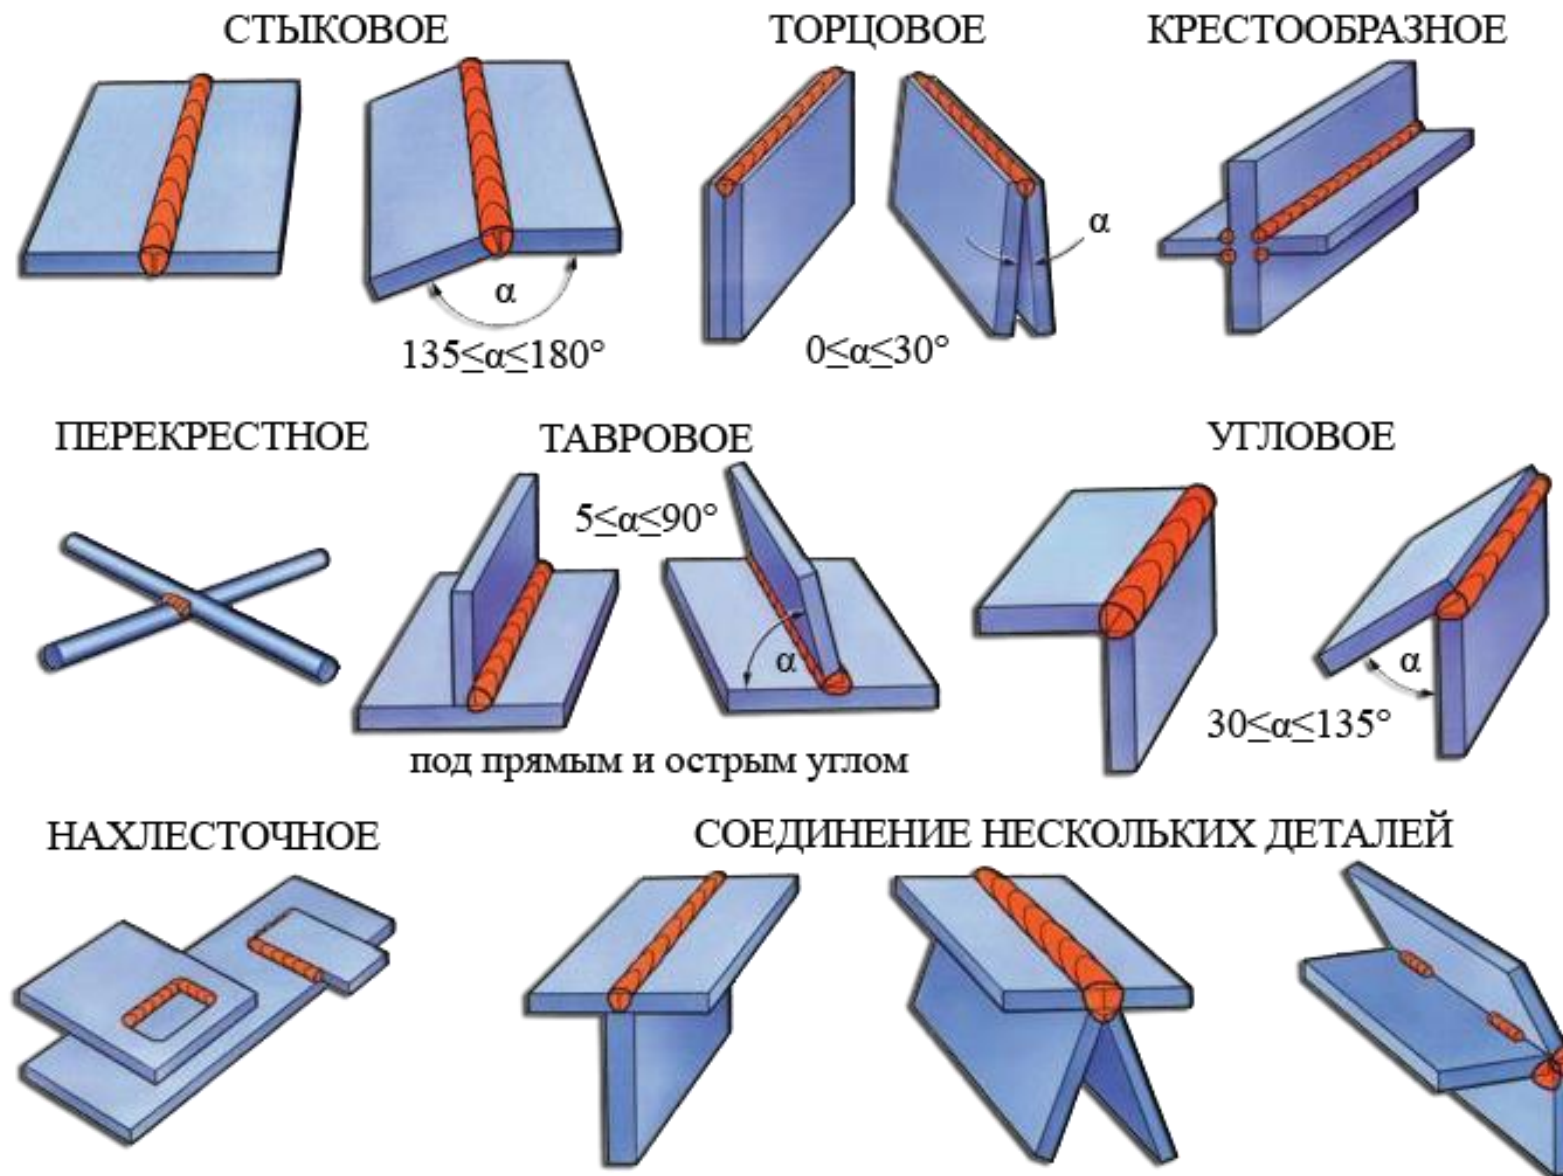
Основные типы сварных соединений по ГОСТ Р ИСО 17659-2009
